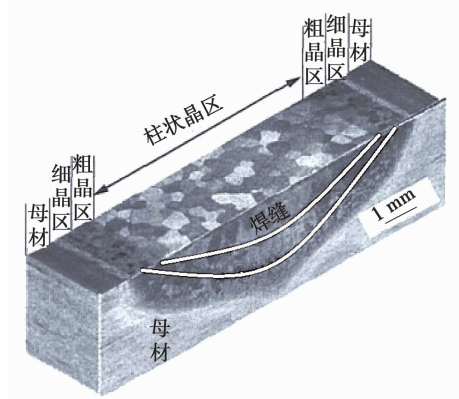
TIG 焊和 ATIG 焊立体宏观组织形貌示意图
